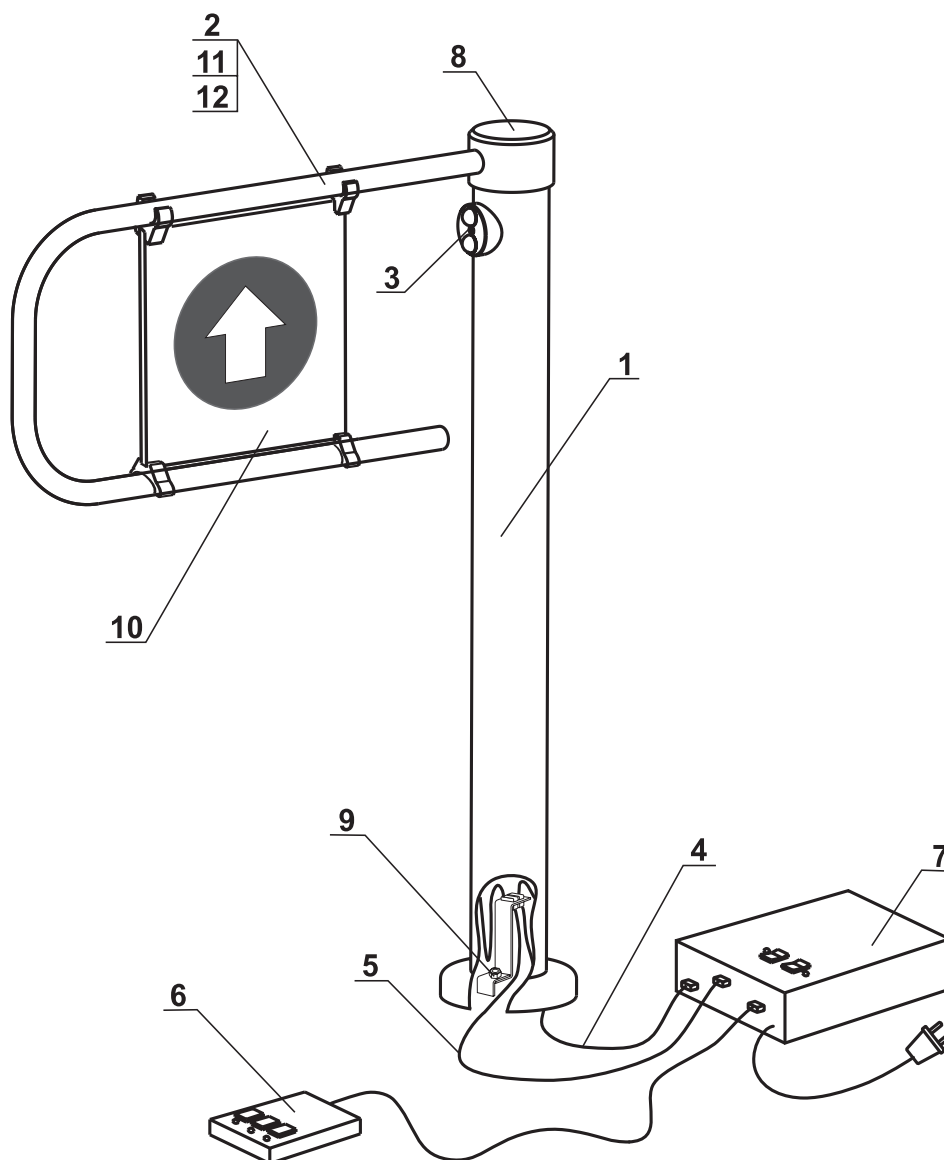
Чертеж общего вида калитки PERCo-WHD-04:
